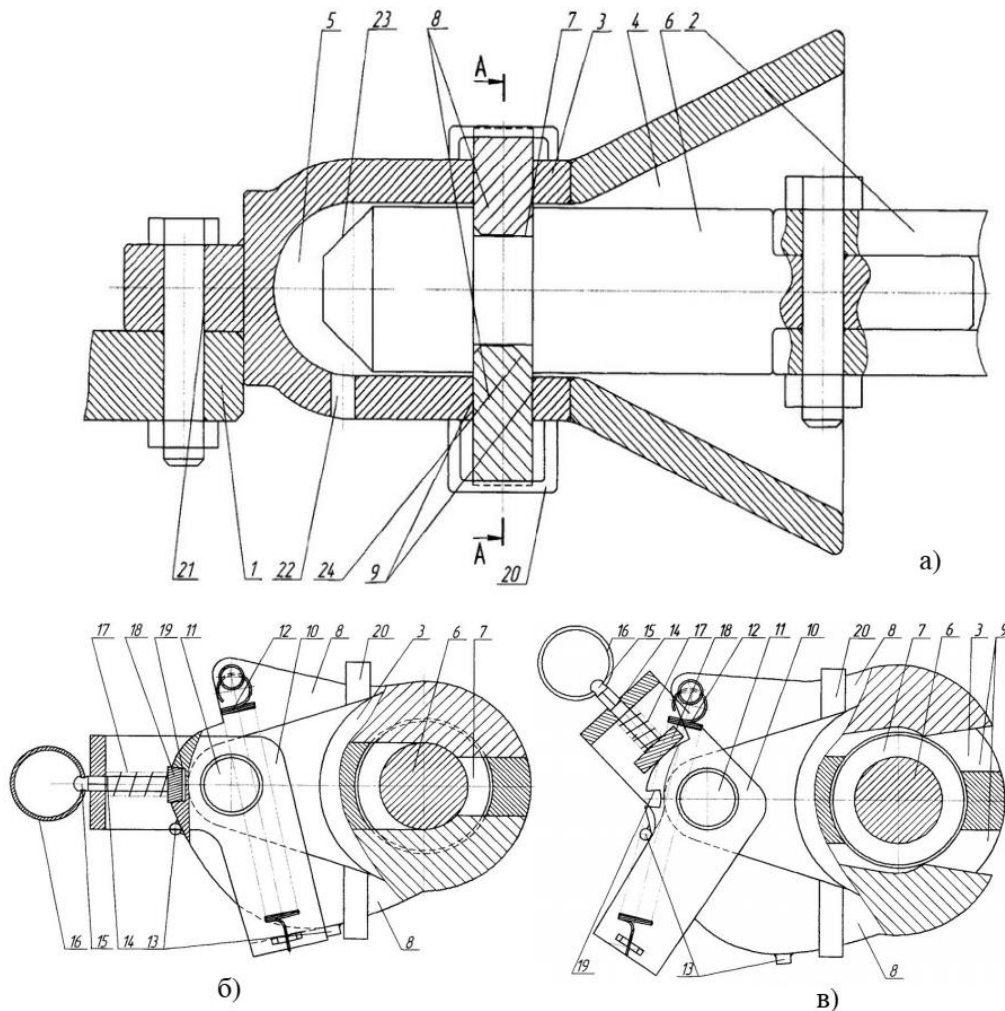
Автоматичний зчпний пристрій тягача: а) загальний вигляд; б) вид збоку в замкнутому стані; в) вид збоку в розімкнутому стані.
